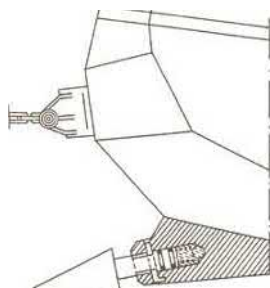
Ковш экскаватора с подвижными зубьями (а.с. № 616371 СССР)
